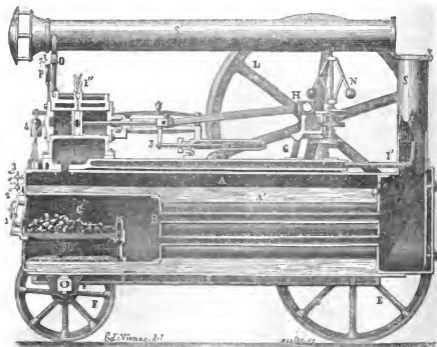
Coupe longitudinale de la machine à vapeur locomobile de M. Cumming, à Orléans.
